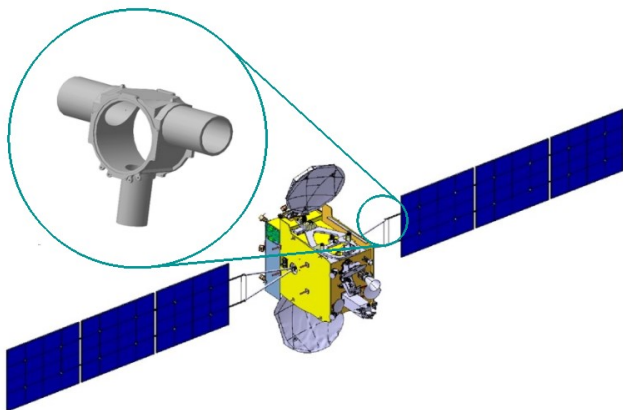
Пример детали из титанового сплава для соединения трубчатых элементов КА
